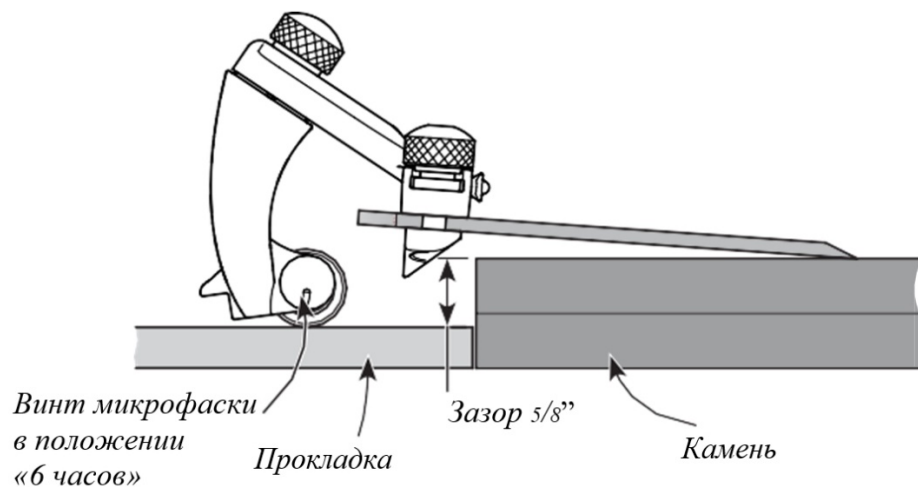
Приспособление для установки очень низких углов задней фаски
